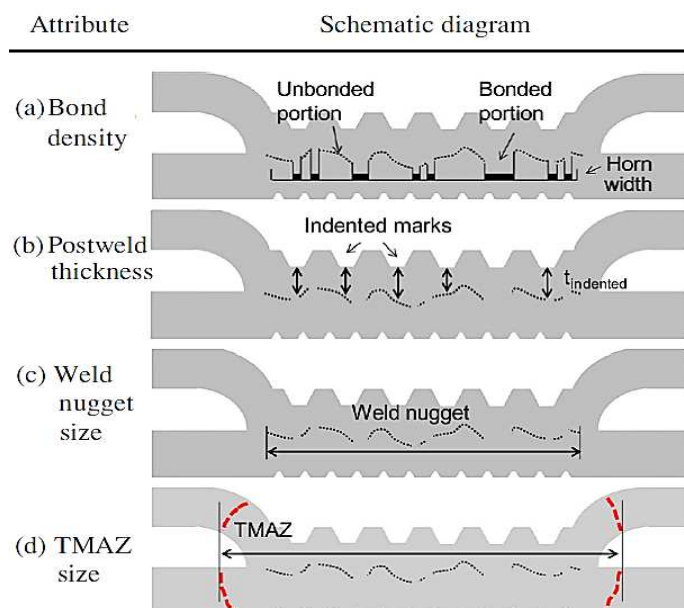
Схематическое изображение характеристик сварного соединения [48]
